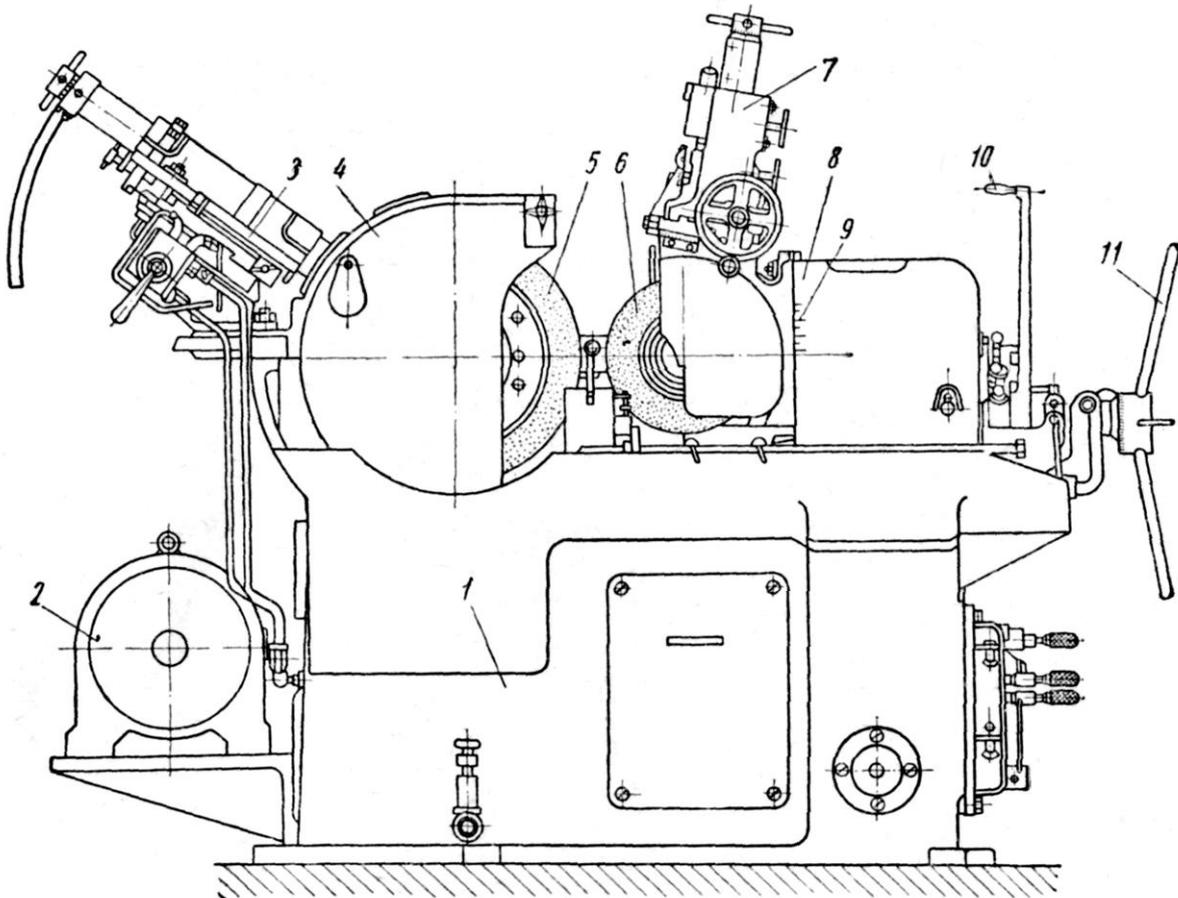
Общий вид бесцентровочно-шлифовального станка
